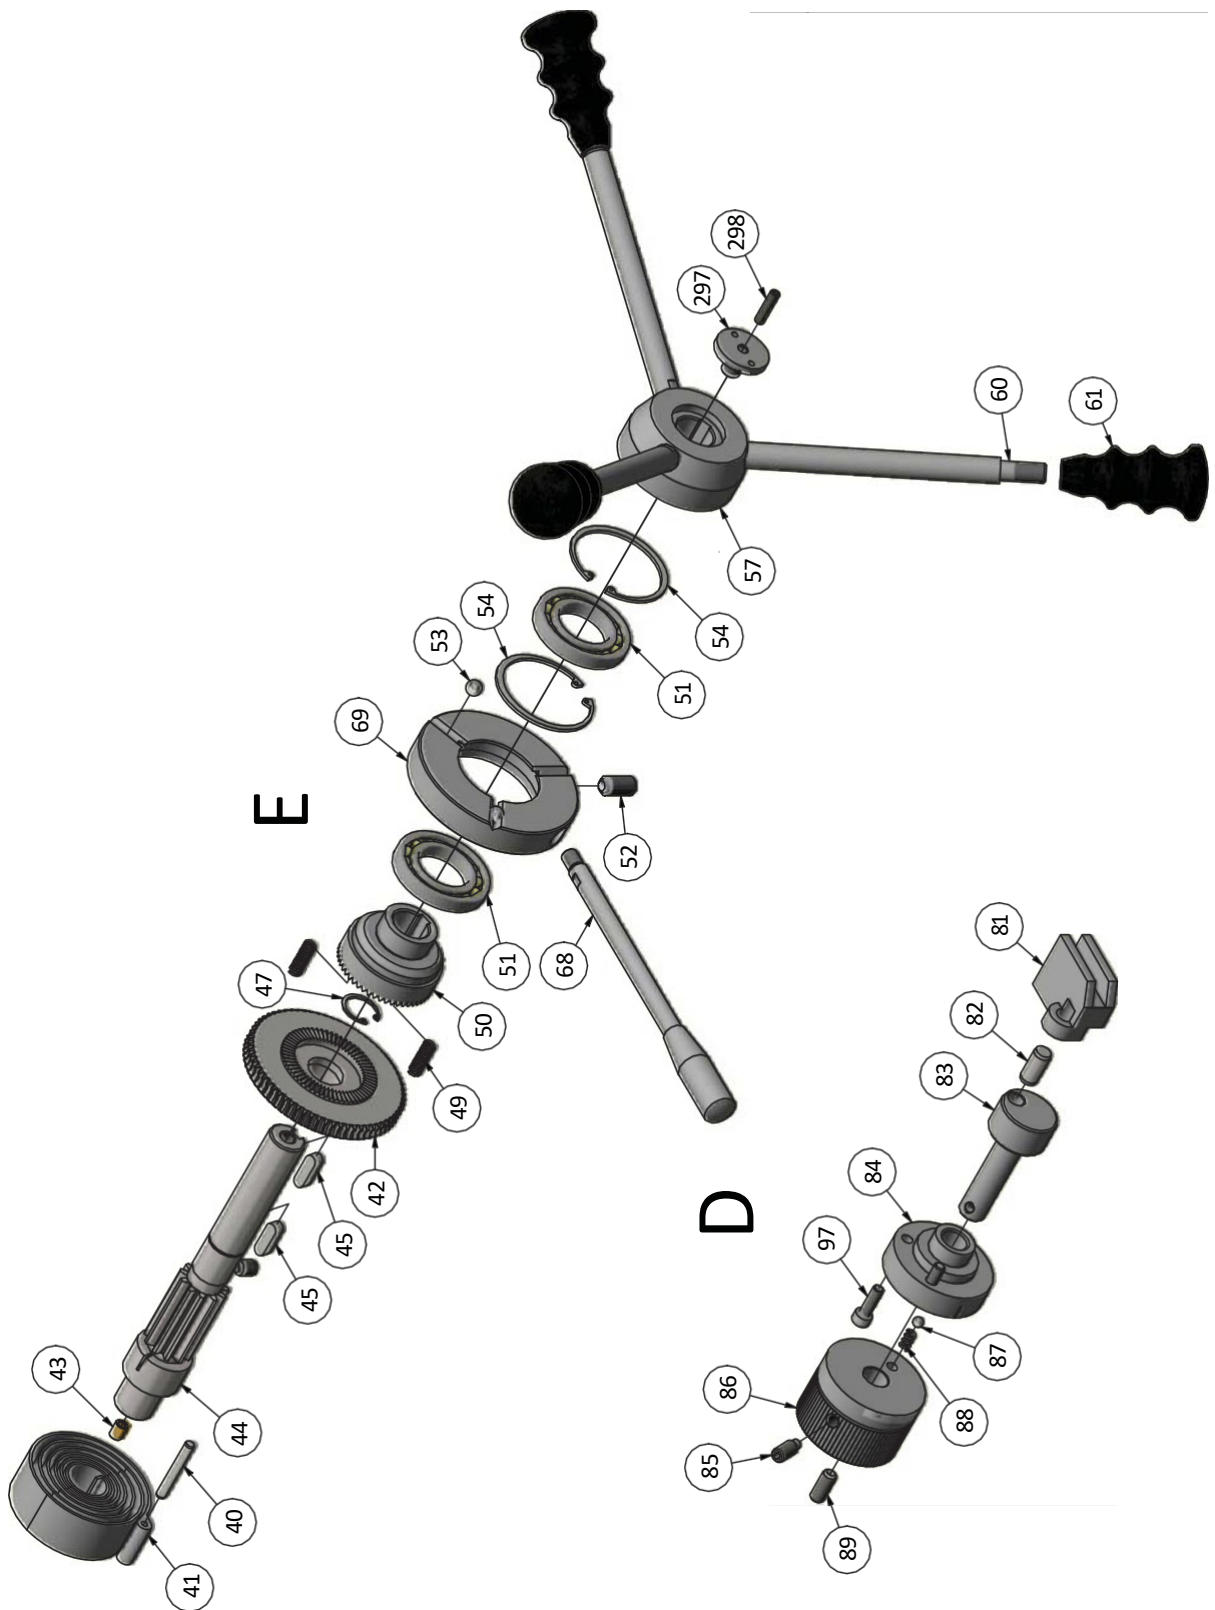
Vorschubgetriebe 2 von 4 - Gearbox 2 of 4
